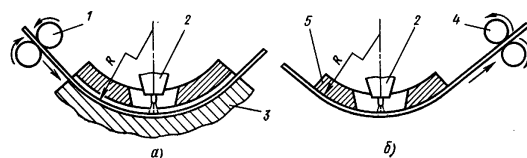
Схемы сварки с непрерывным деформированием:
